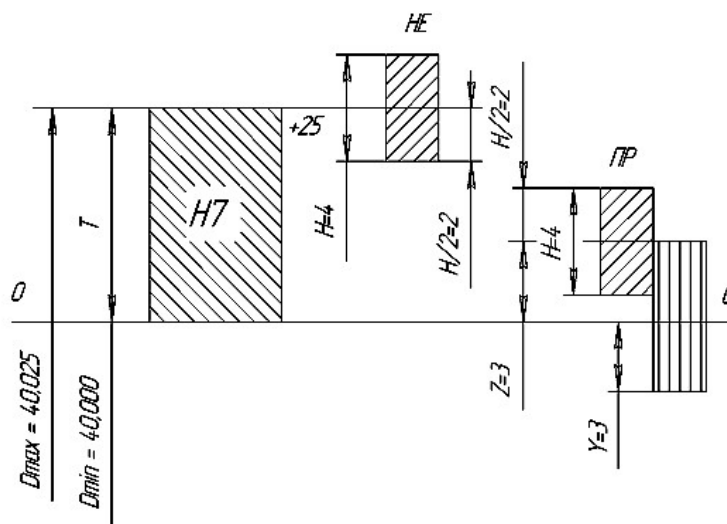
Схема розташування полів допусків для розміру  $\varnothing 40H7^{+0,025}$
